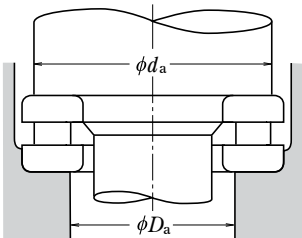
Diâmetro da Superfície de Suporte do Rolamento Axial de Rolos
